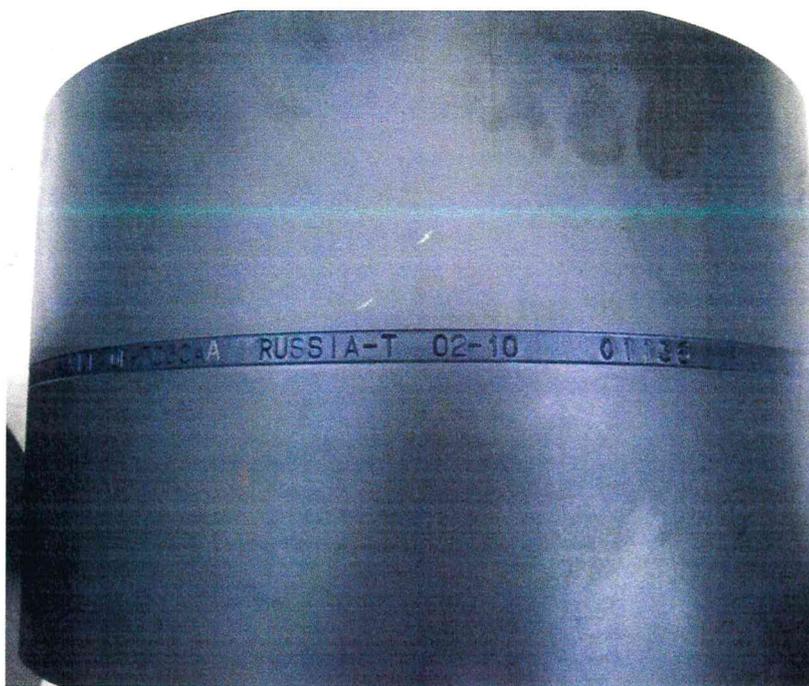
Маркировка наружного кольца кассетного подшипника торговой марки SKF.
